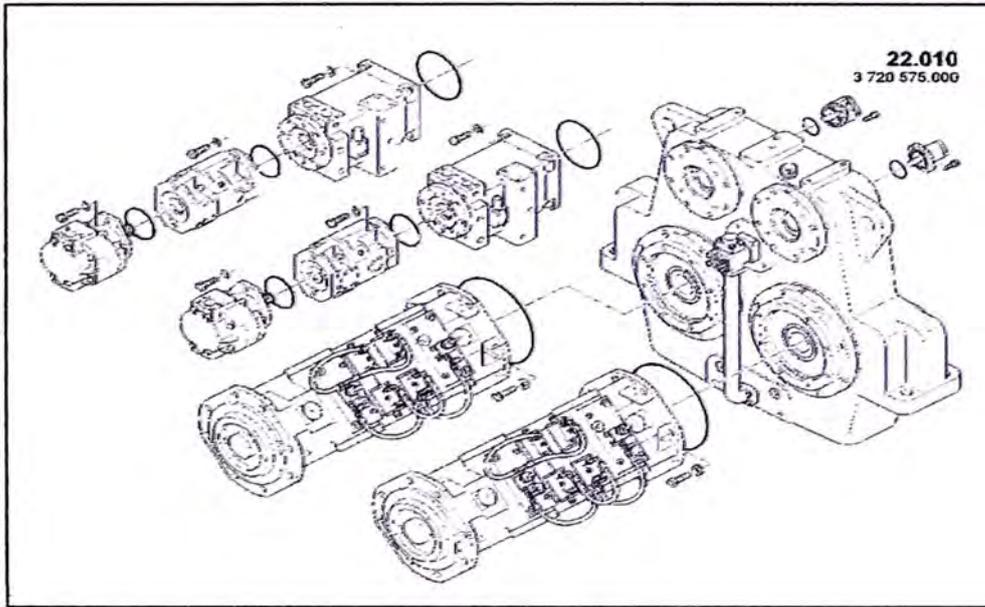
Caja Reductora de Bombas acoplada al motor 3512C
